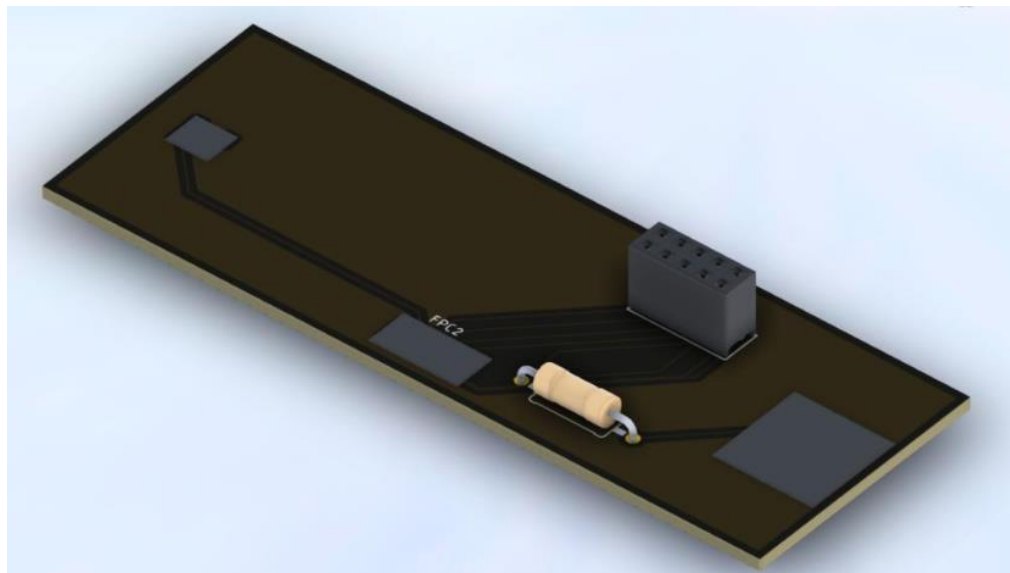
Diseño 3D de la PCB del láser y fotodiodo.
